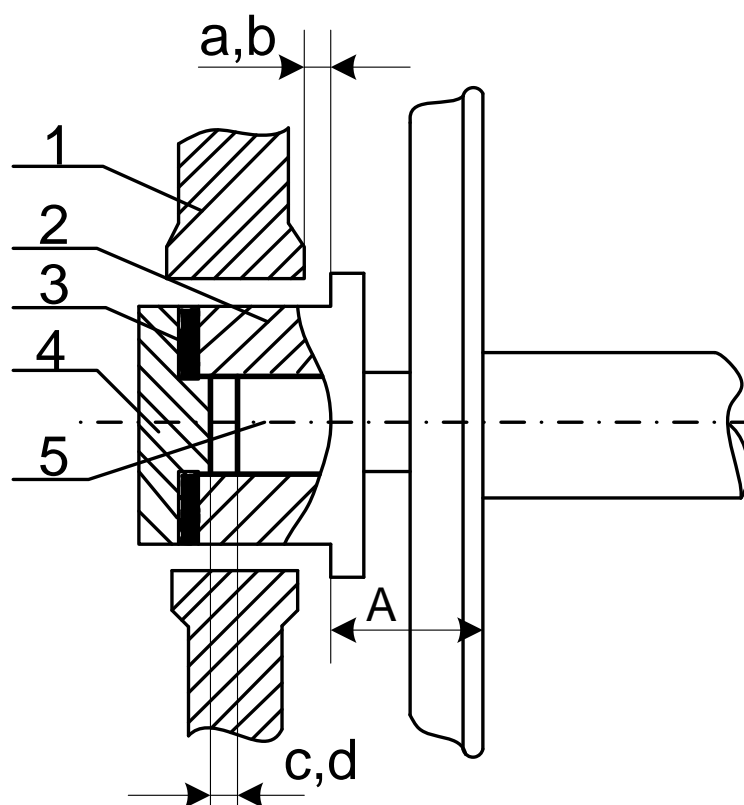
Регулировка свободного разбега колесных пар: 1 – рама тележки; 2 – корпус буксы; 3 – прокладки; 4- упор; 5 – шейка оси
